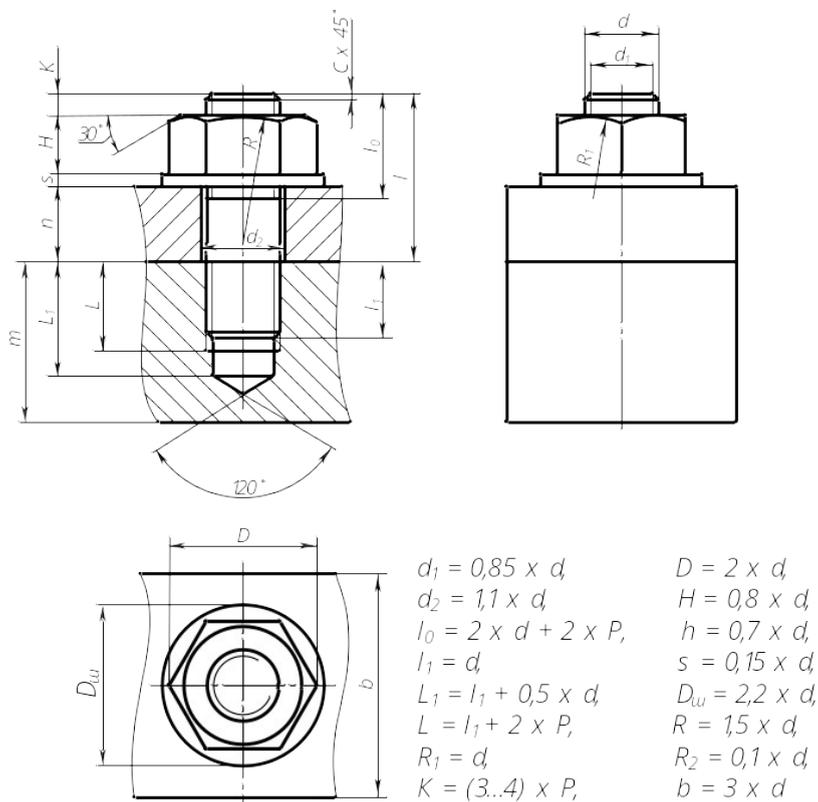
Условное изображение соединения деталей шпилькой и соотношения размеров деталей
